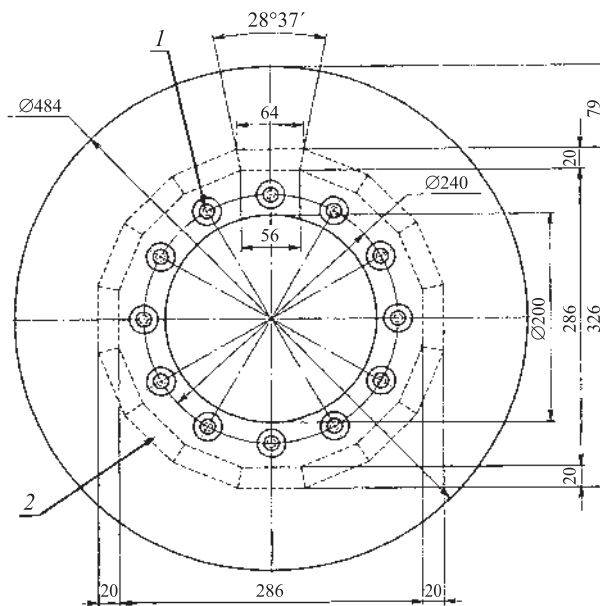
Размещение КЭНов в печи (вид сверху): 1 — КЭН; 2 — футеровка
